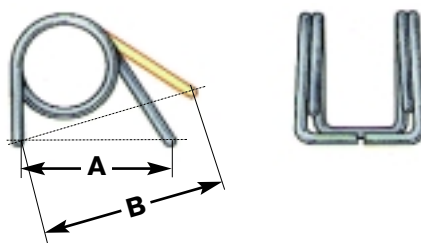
Схема проверки пружины рычага: А – размер в свободном состоянии; В – размер под нагрузкой  $(5,5 \pm 0,6)$  кгс
